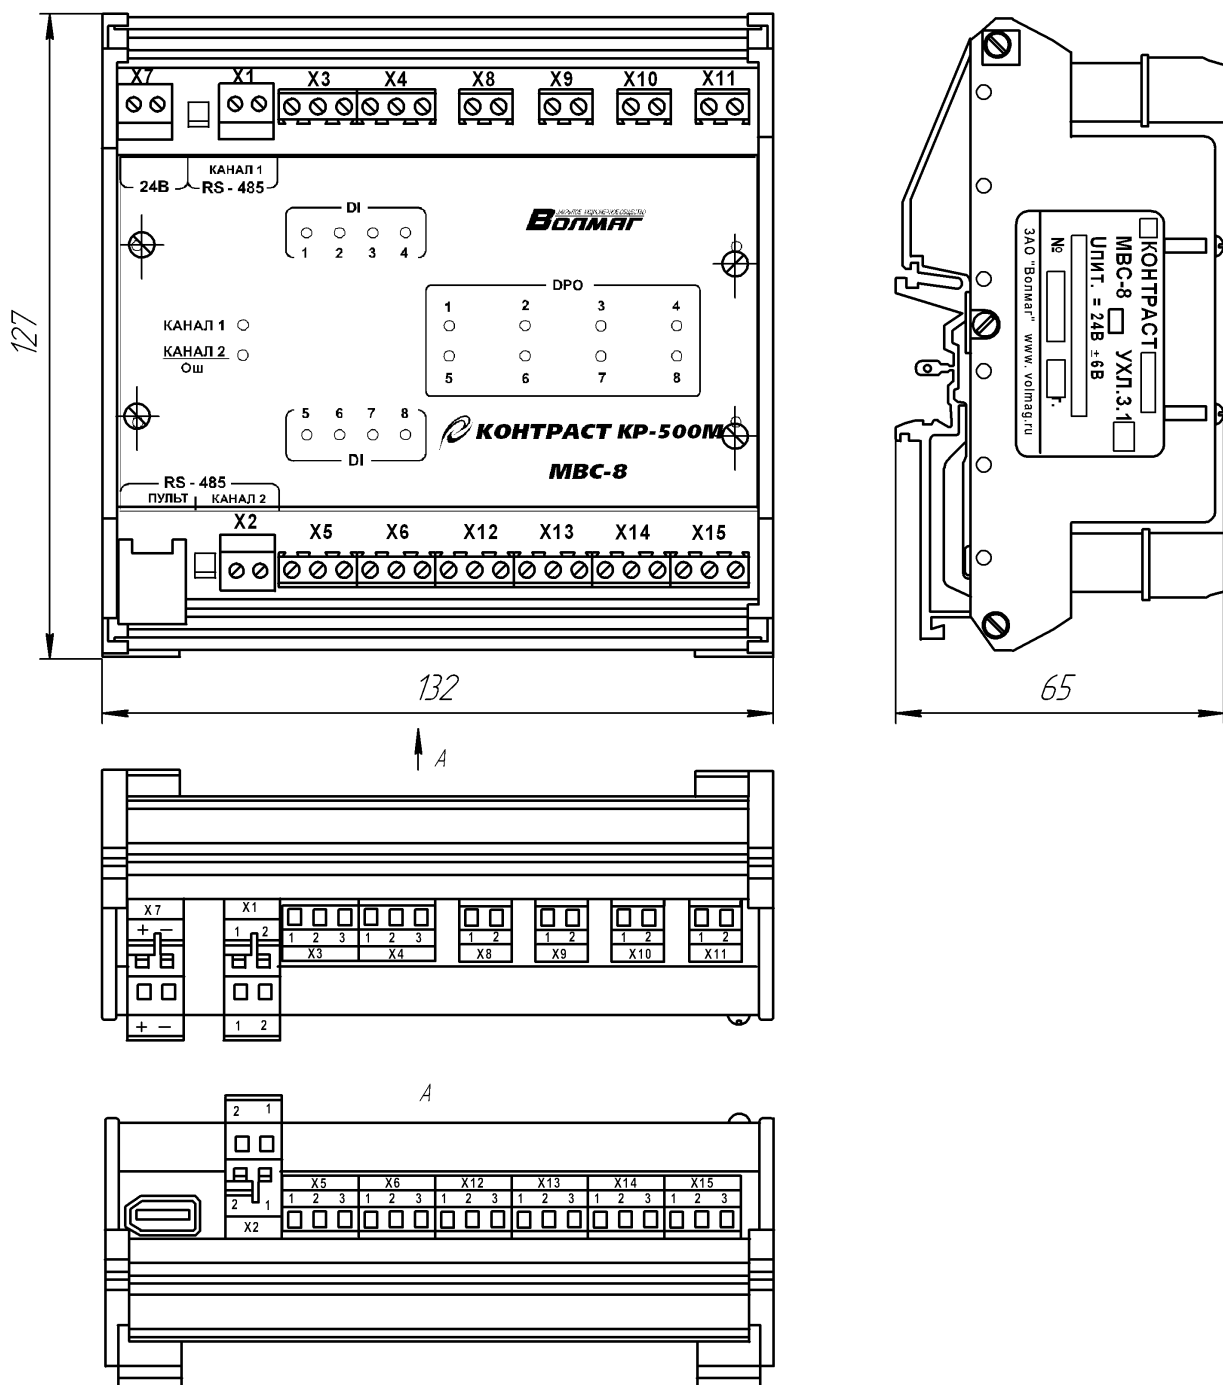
Внешний вид и габаритно-установочные размеры модуля MBC-8-02 (-03)
